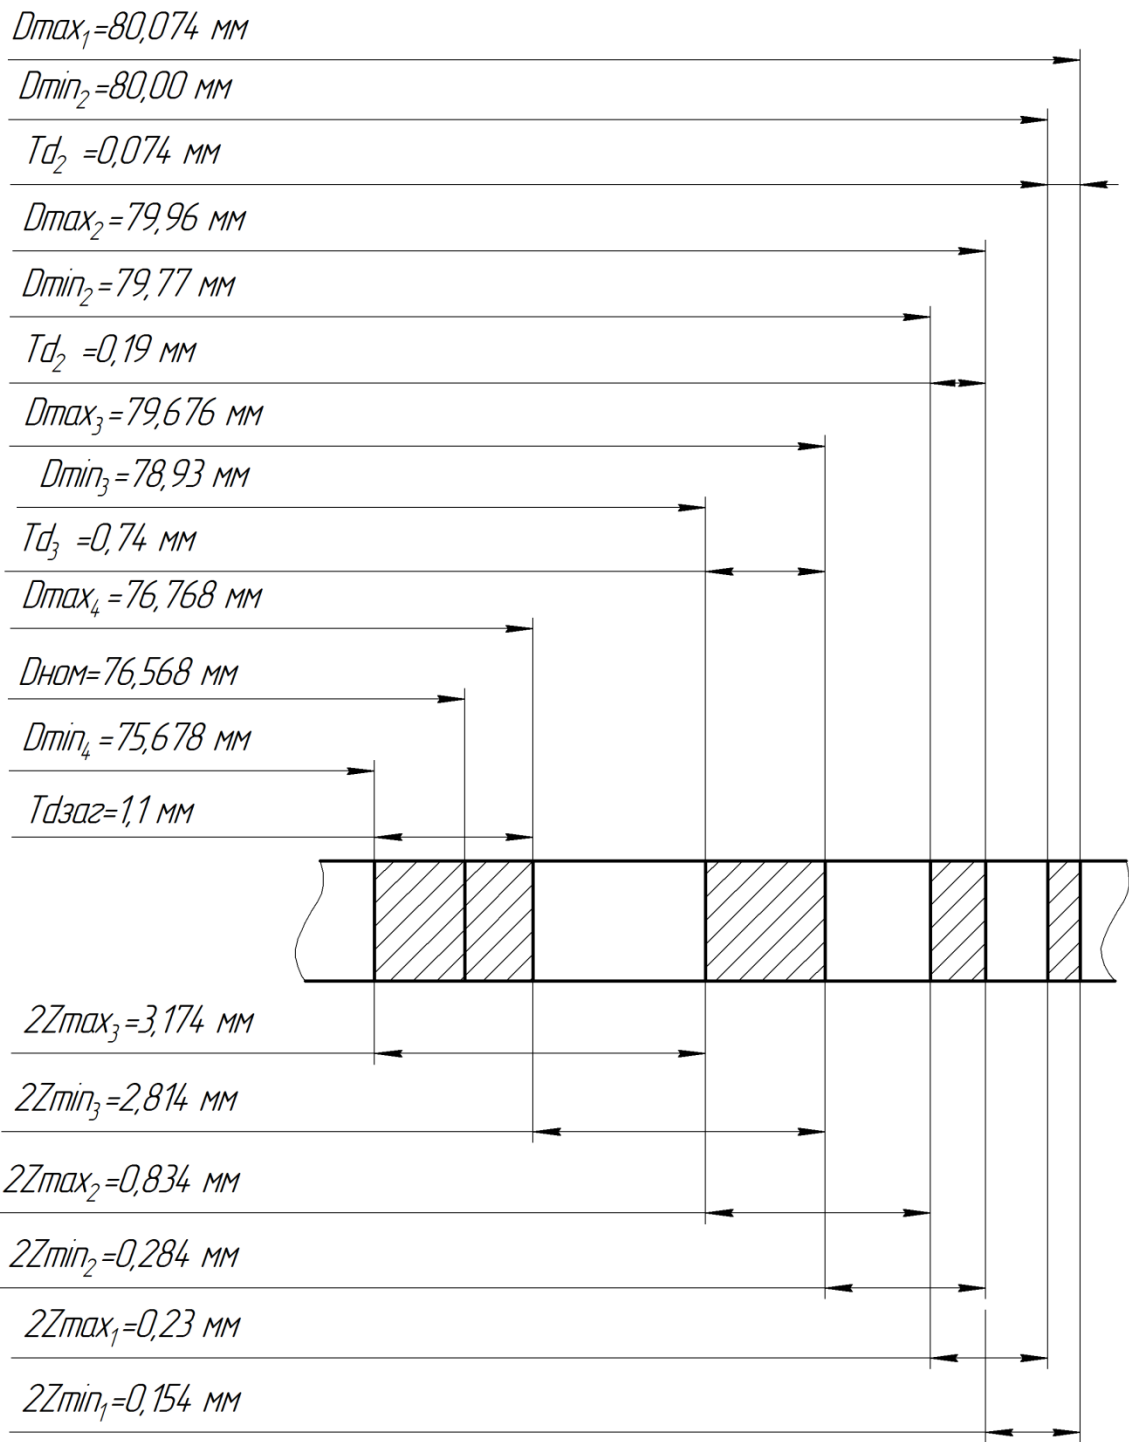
Схема розміщення допусків і припусків на обробку поверхні $\varnothing 80H9$
